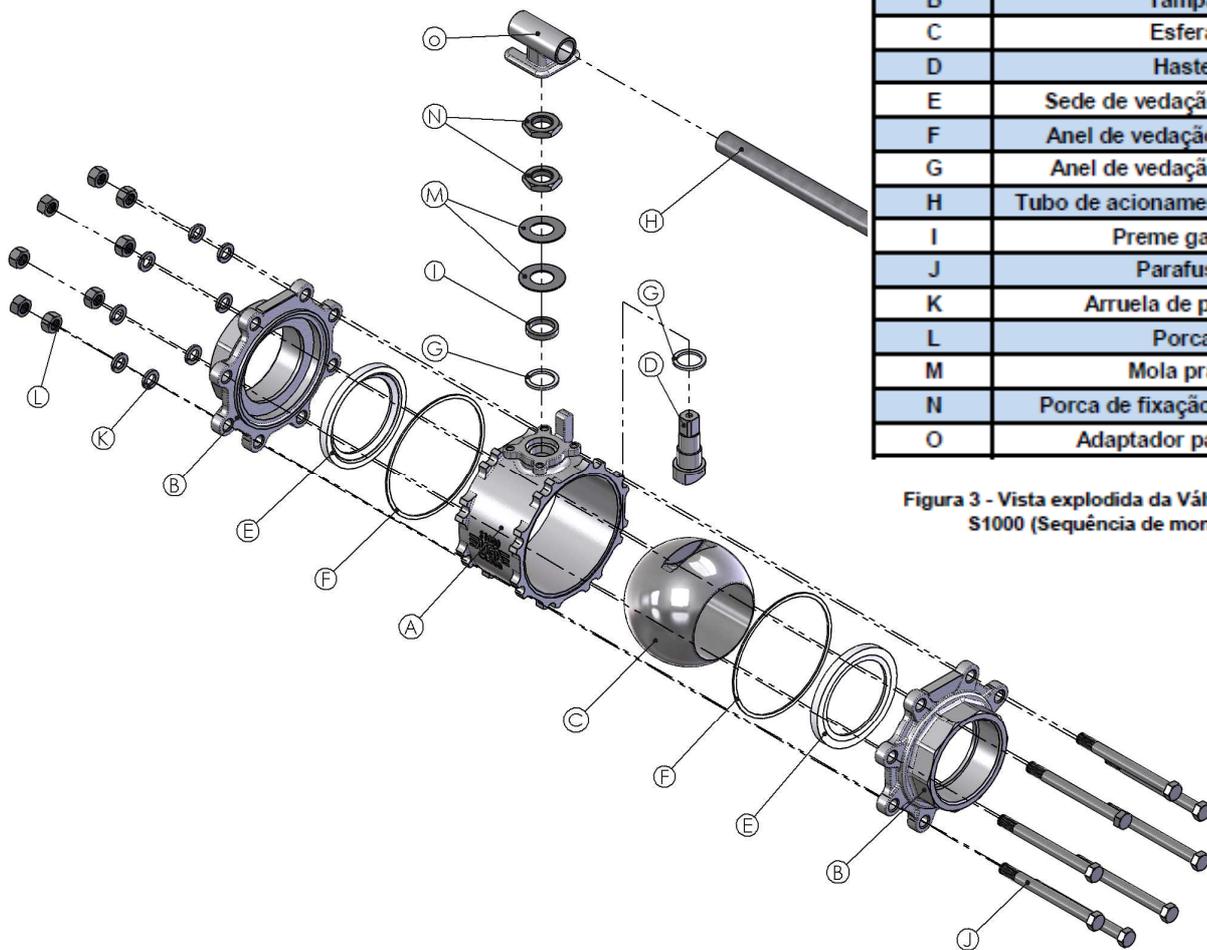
Vista explodida da Válvula de Esfera S1000 (Sequência de montagem)
